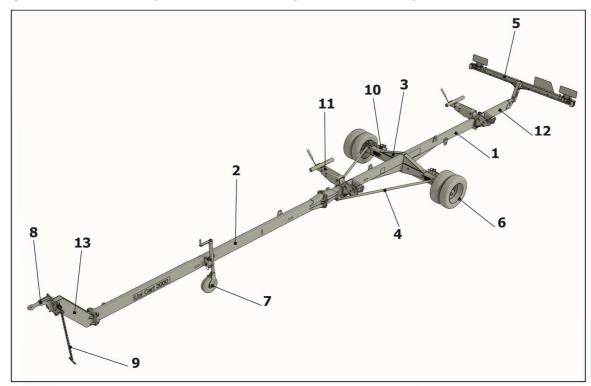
Общий вид приспособления ППА-700-01 "Uni Cart 3000"
